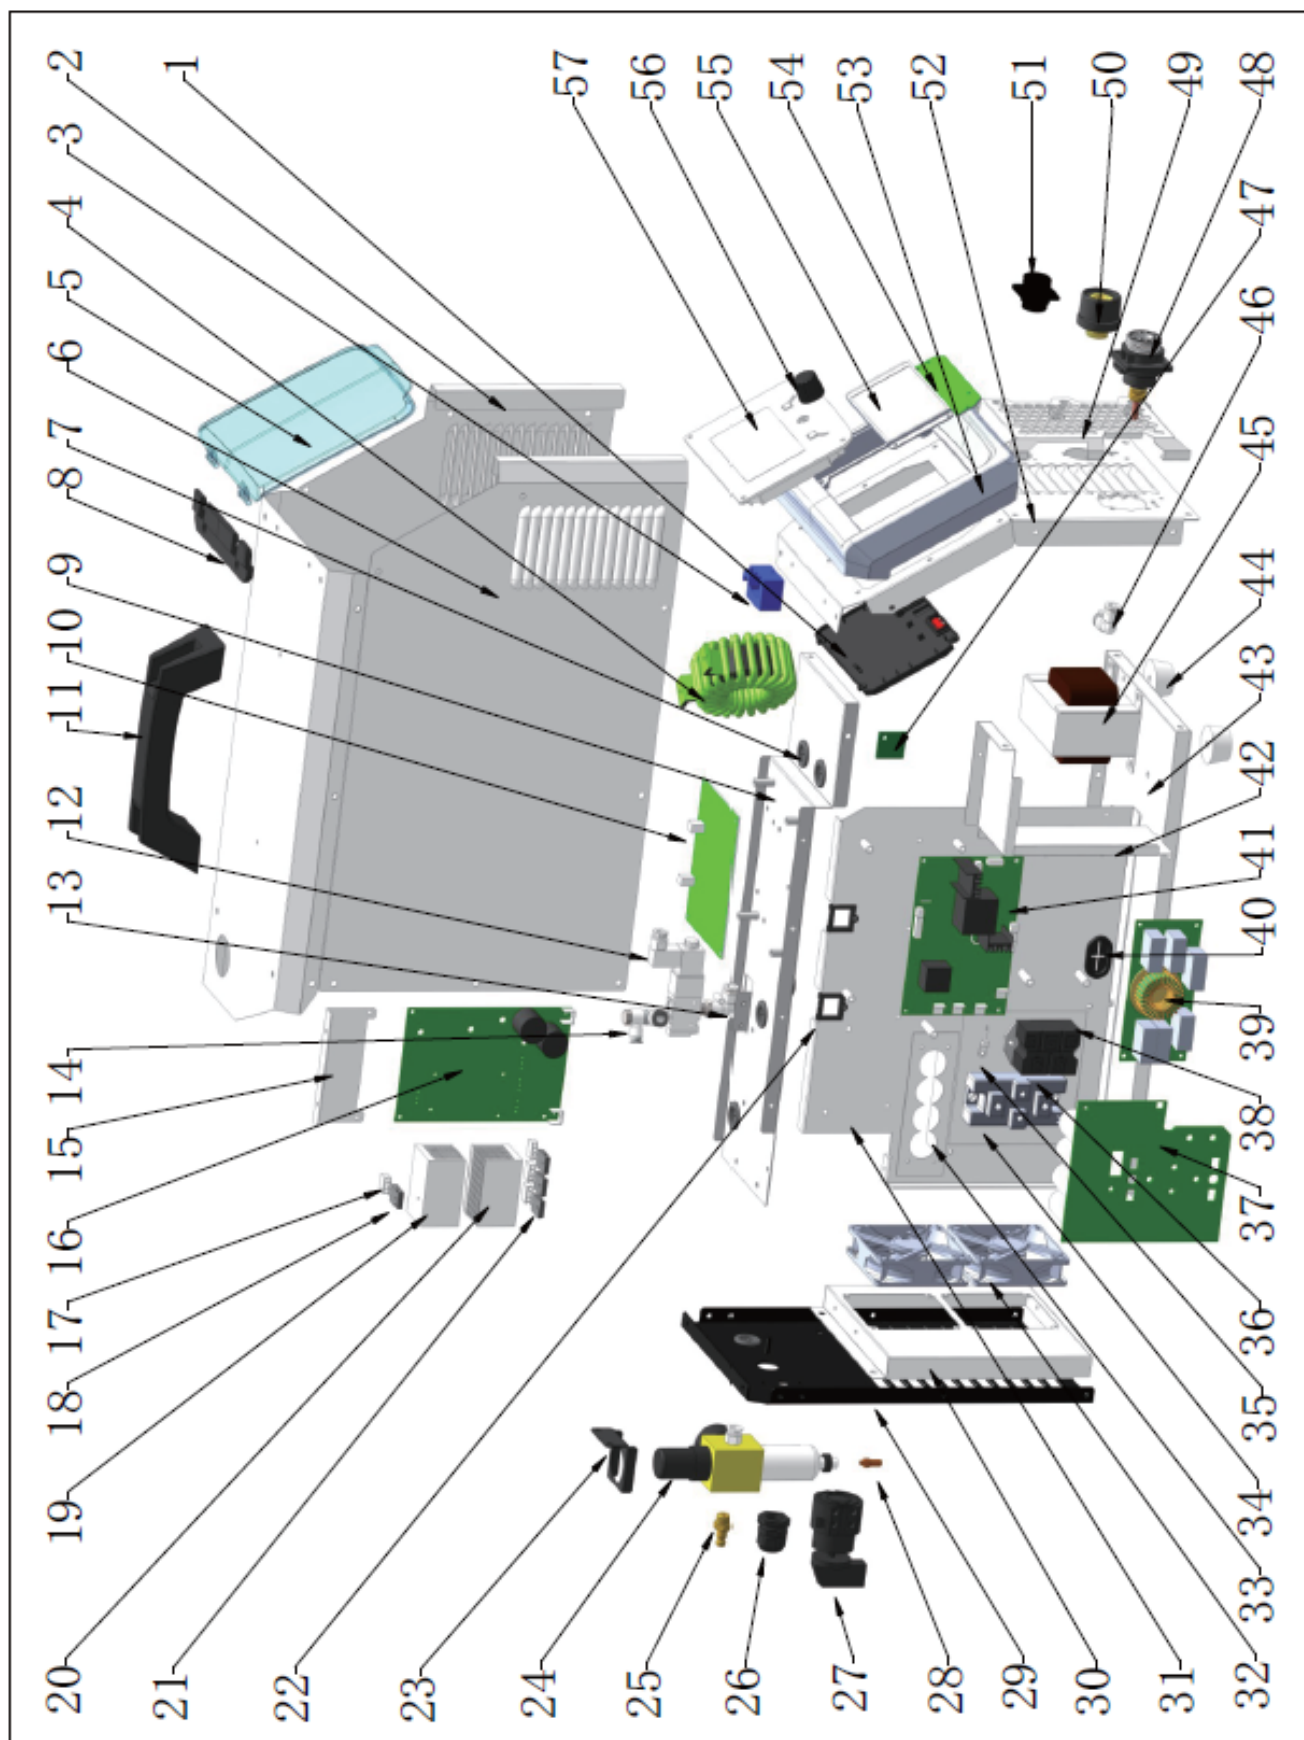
Ersatzteilzeichnung CRAFT-CUT 63 CNC LCD
